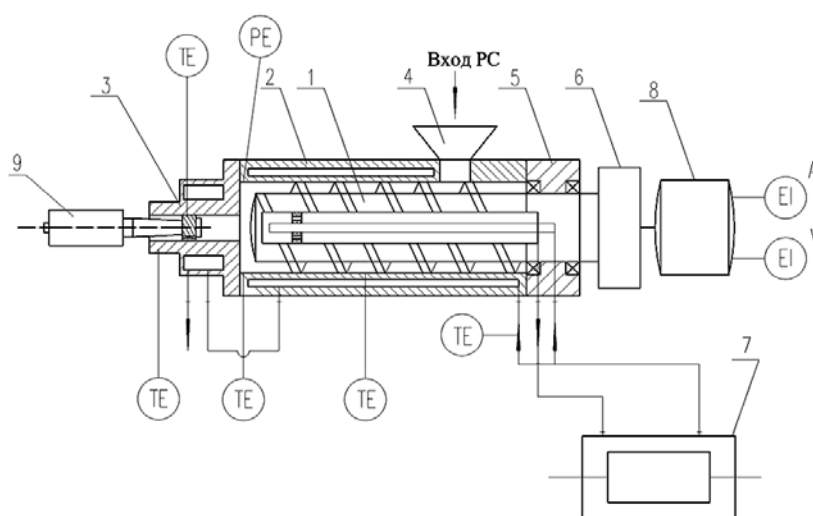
Экспериментальная установка для исследования процесса профилирования длинномерных заготовок из резиновой крошки: 1 – шнек; 2 – цилиндр; 3 – формующая головка; 4 – загрузочное устройство; 5 – привод шнека; 6 – редуктор; 7 – термостат; 8 – электродвигатель; 9 – ультразвуковой преобразователь; TE – датчики температуры; PE – датчик давления; А – амперметр; V – вольтметр
